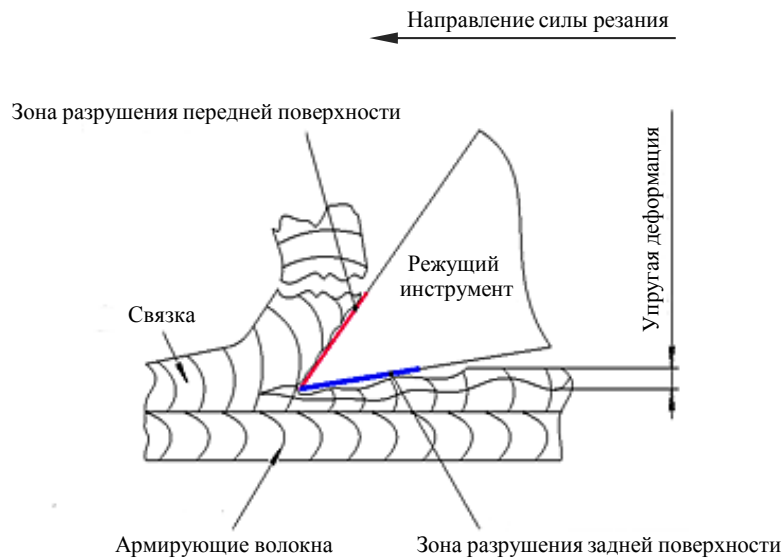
Схема износа поверхностей режущего инструмента при лезвийной обработке металлического композиционного материала
